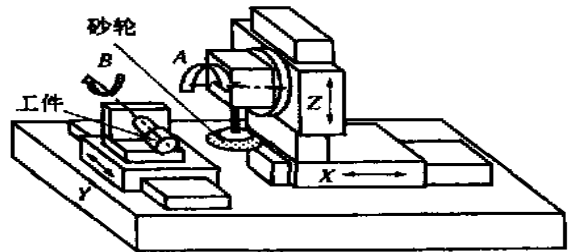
工件平动、砂轮摆动 CNC 五联动工具磨床(B 型)
